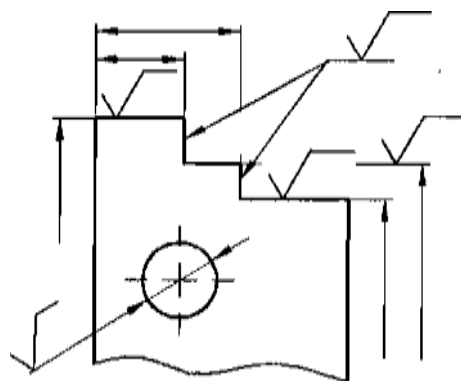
Обозначение шероховатости поверхности на детали
